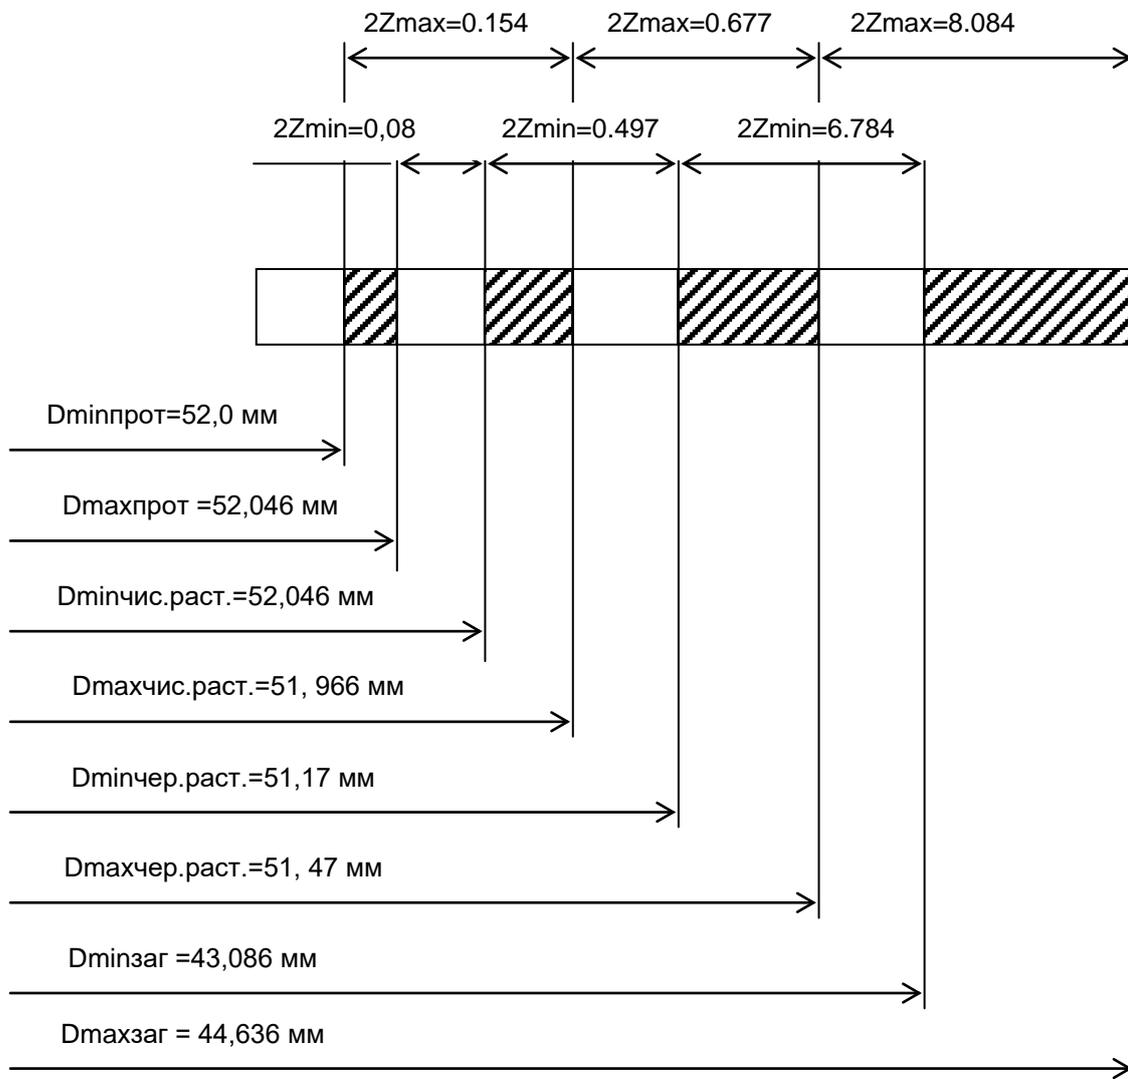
Схема графического расположения припусков и допусков на обработку поверхности  $\varnothing 52H8$  зубчатого колеса.
